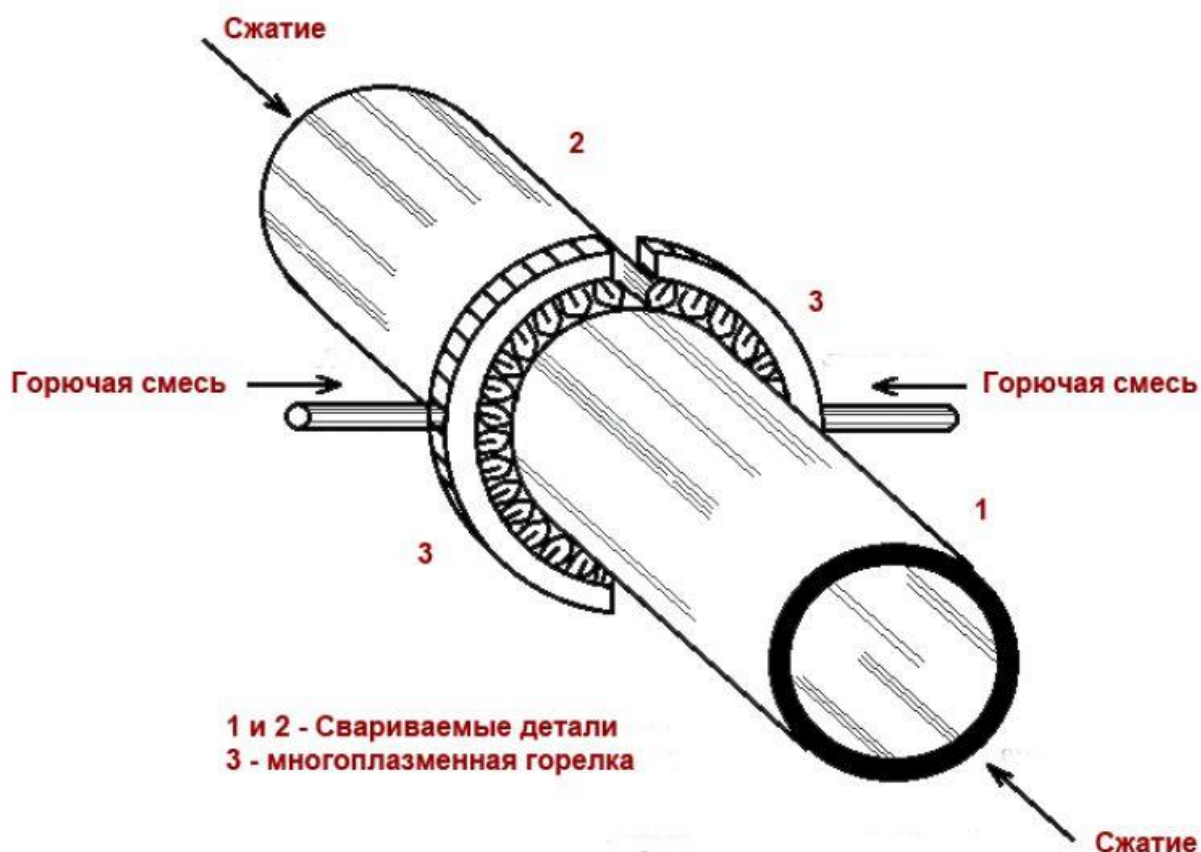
Газопрессовая сварка [4, с. 87].
